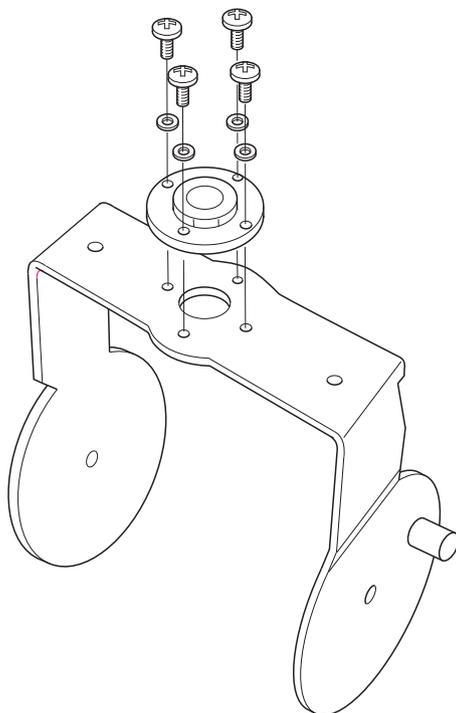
Fixation de la plaque au support de suspension en cas de montage sur un trépied
